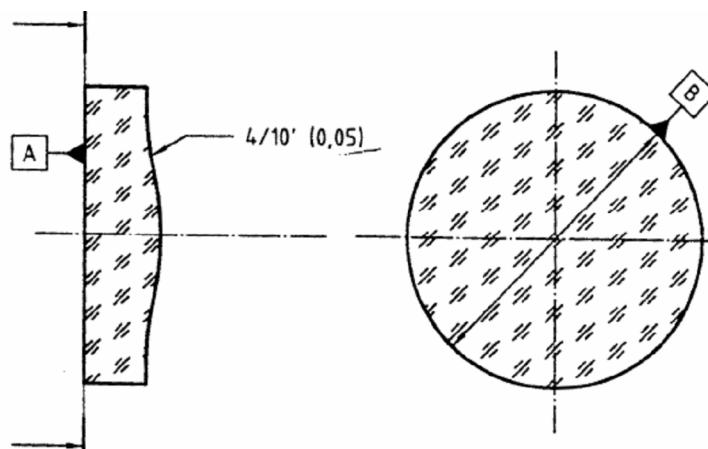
Допуск на центрировку асферичної поверхні
